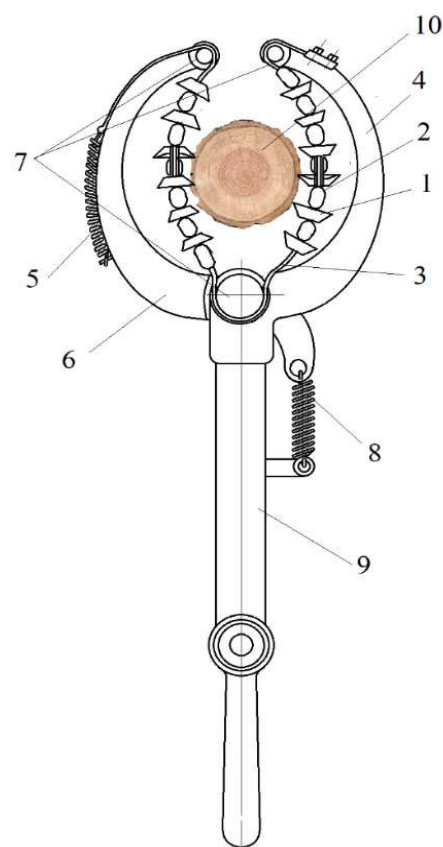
Взаимодействие пружинящего устройства для кольцевания с деревом, подлежащим удалению: 1 – режущий орган, 2 – цилиндрические вставки, 3 – гибкий канат, 4 – неподвижный зажимной рычаг, 5 – натяжная пружина, 6 – подвижный зажимной рычаг, 7 – блок, 8 – прижимная пружина, 9 – корпус, 10 – дерево
